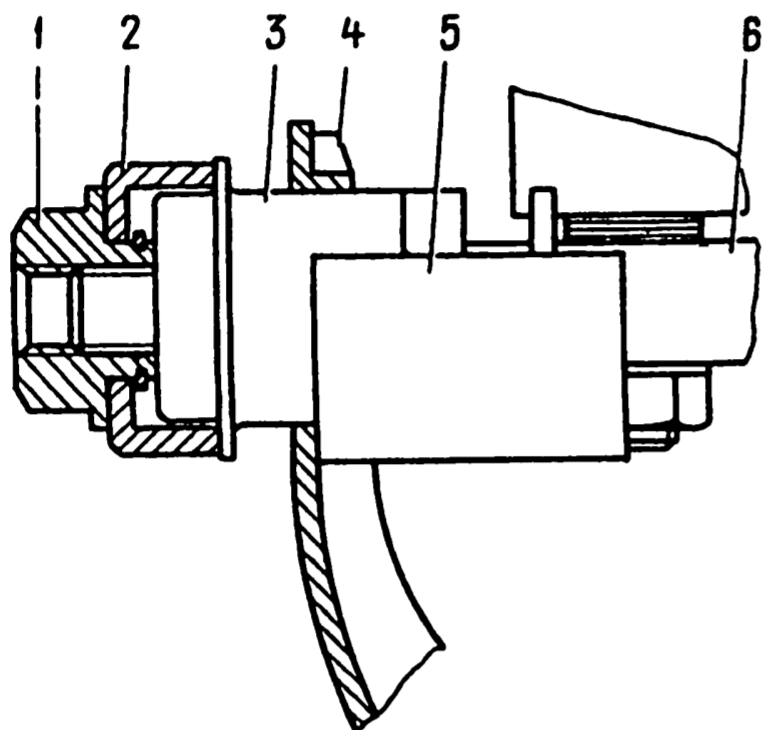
Схема запрессовки шарнира нижнего рычага с помощью приспособления 02.7823.9501: 1 - гайка; 2 - кольцо; 3 - шарнир; 4 - нижний рычаг; 5 - упор; 6 - ось нижнего рычага
